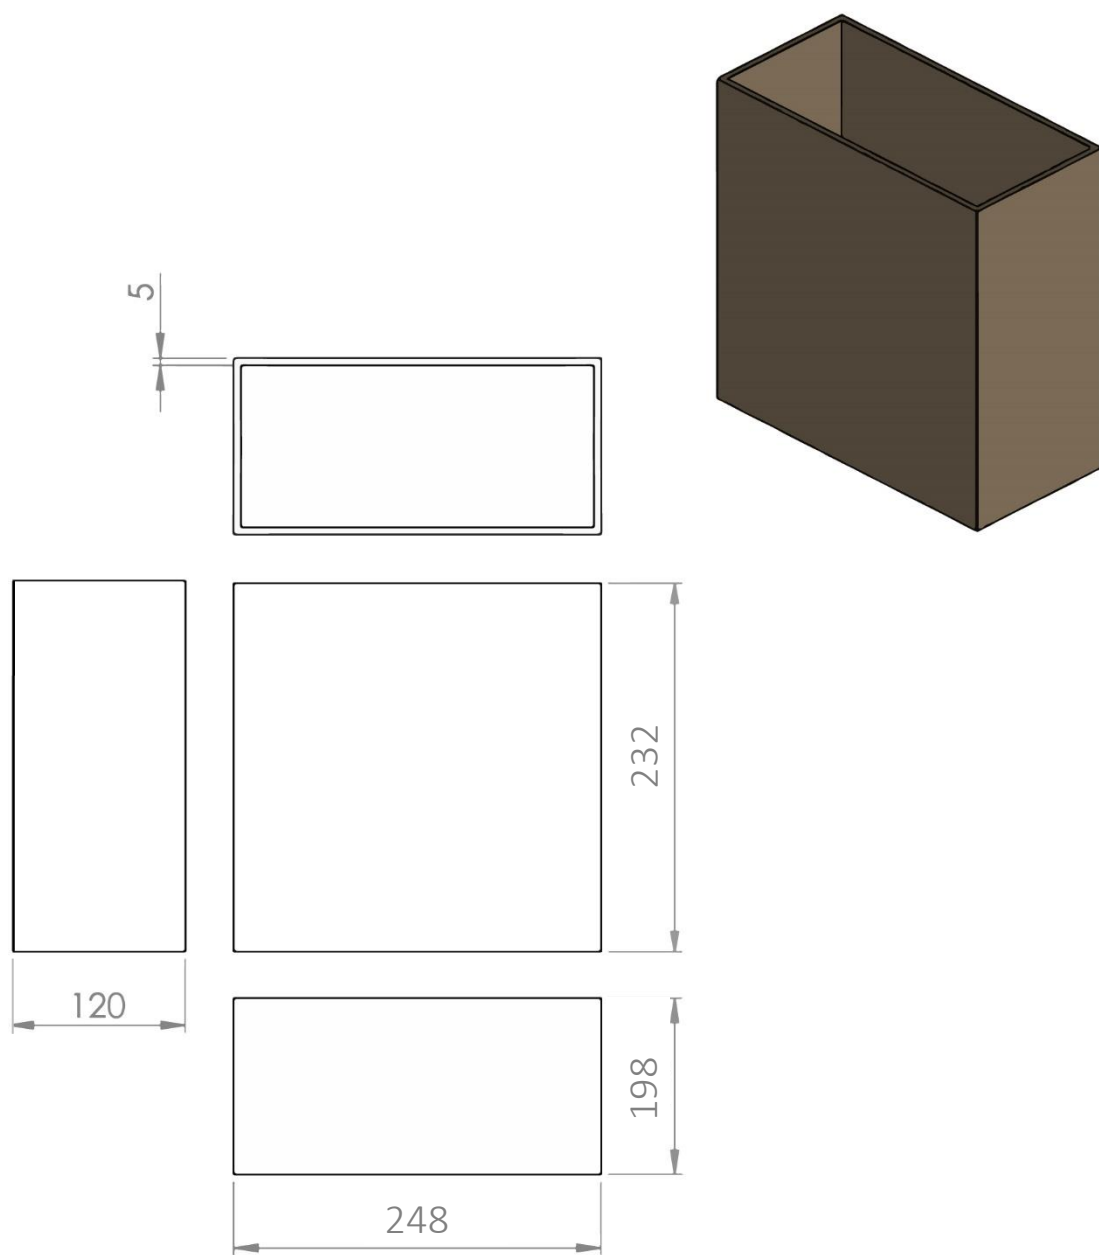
Dimensões gerais para a parte de pasta de papel com fibra de sisal (mm)
